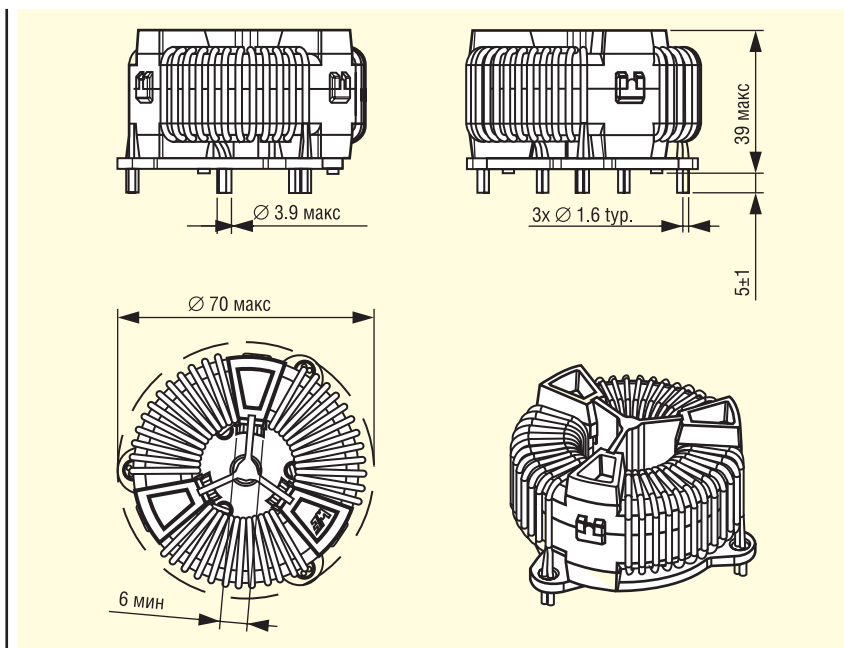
Габаритные размеры дросселей WE-TPB HV [2]
